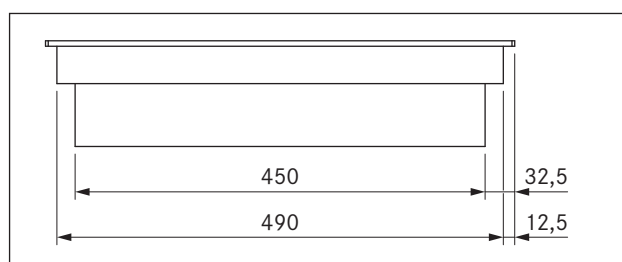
Dimensões do aparelho CKIW, vista lateral
